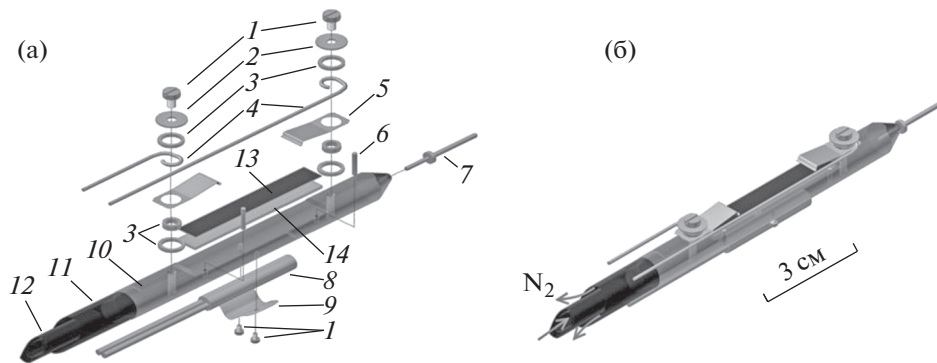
Держатель образца. 1 – винт; 2 – шайба; 3 – диэлектрические втулки; 4 – токопровод; 5 – контакты; 6 – ограничители; 7 – ограничительный элемент; 8 – платиновое термосопротивление ЧЭП-2888; 9 – крепление; 10 – держатель образца; 11 – шток; 12 – коаксиальная трубка; 13 – образец; 14 – диэлектрическая пластина.
